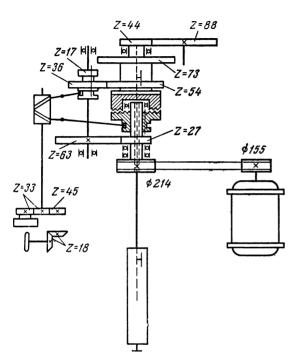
Кинематическая схема привода главного движения станка модели 2 B440
